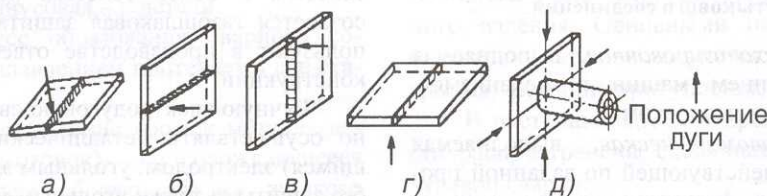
Схема пространственного положения сварных швов:
